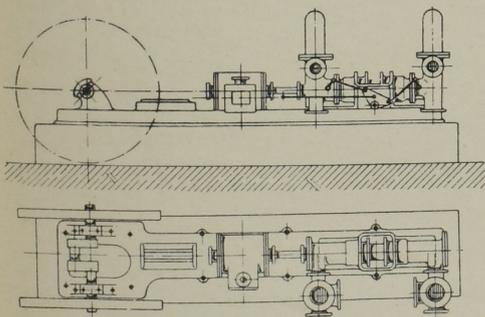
Grundriss. Massst. 1:60.
